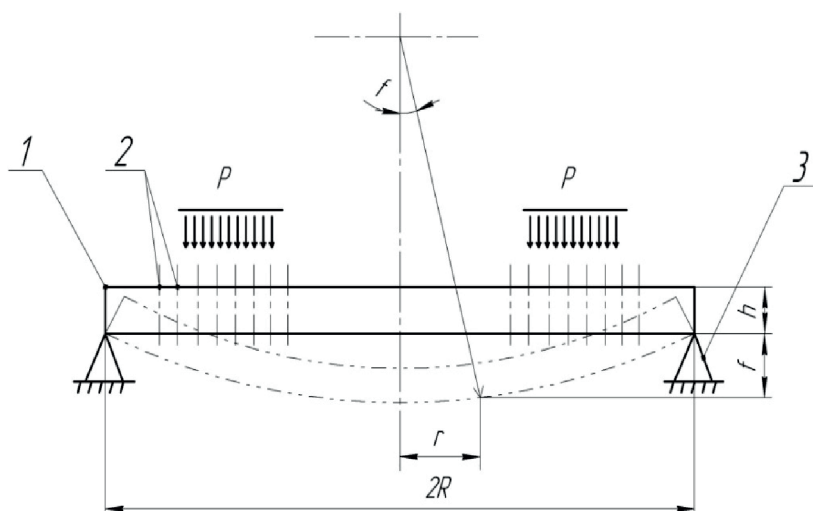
Схема деформаций корпуса сплошной матрицы с шарнирным закреплением по наружному контуру: 1 – корпус матрицы; 2 – формующие отверстия; 3 – опора; φ – угол поворота к оси симметрии матрицы; f – прогиб центра матрицы; h – высота (толщина) корпуса матрицы; P – давление
